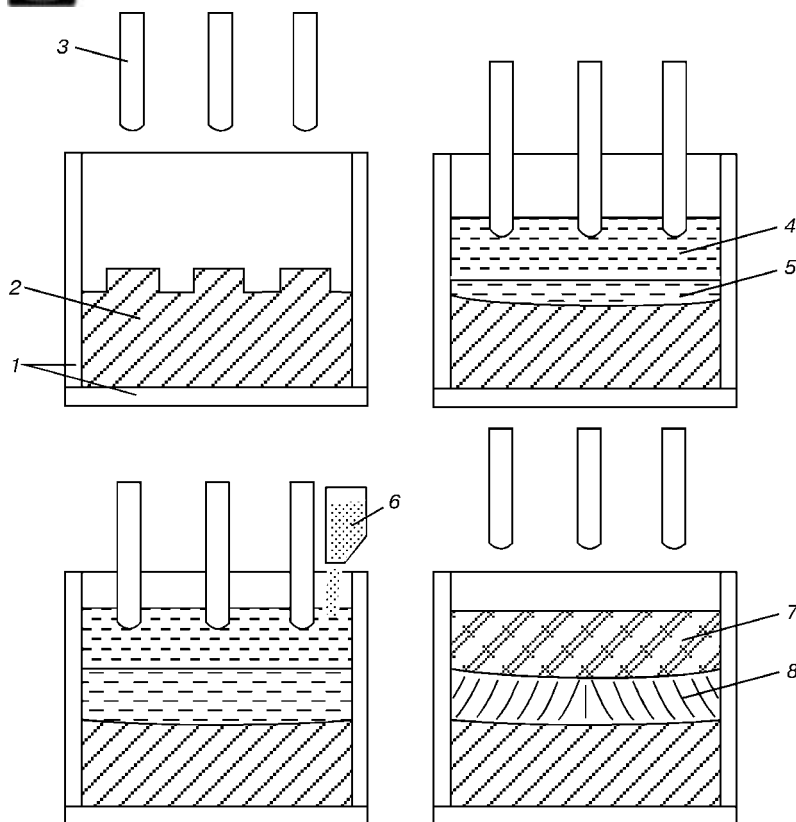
Схема электрошлаковой наплавки штампов: 1 — водоохлаждаемые панели; 2 — изношенный штамп; 3 — нерасходуемый электрод; 4 — шлаковая ванна; 5 — металлическая ванна; 6 — бункер со стружкой; 7 — твердый шлак; 8 — наплавленный слой
